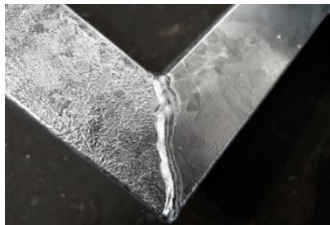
Горячеоцинкованный сварной шов реактивных и неактивных строительных сталей
